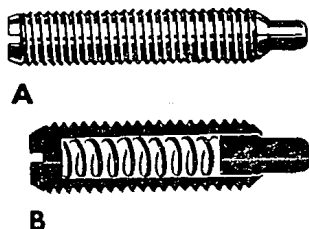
Tornillo con resorte incorporado para el movimiento de un diente único.
